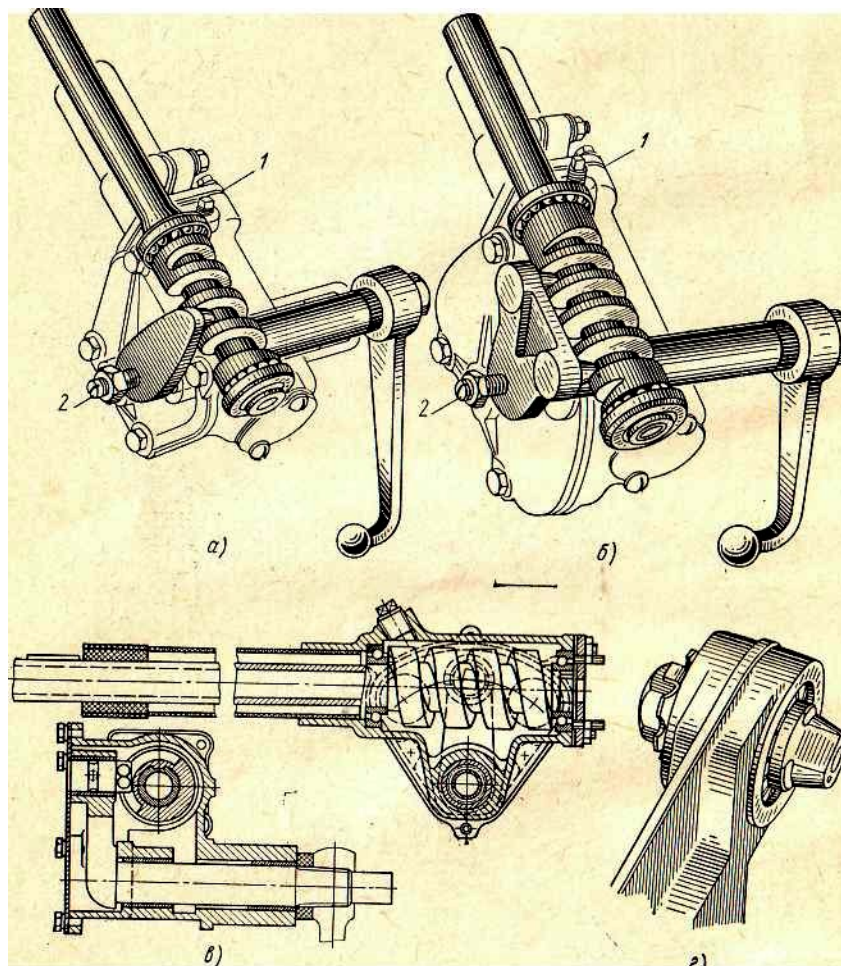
Рулевые механизмы с кривошипной передачей и скользящими Пальцами
